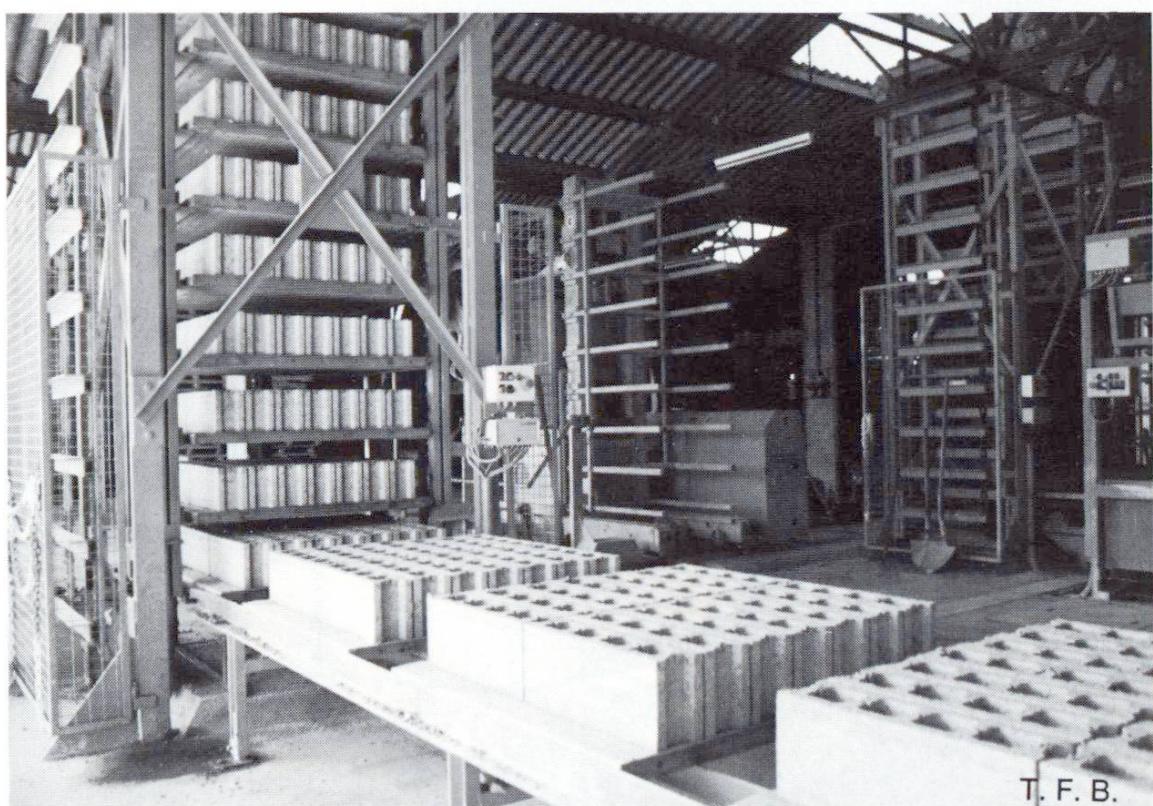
Produktion von Beton-Mauersteinen mit modernen Maschinen.
